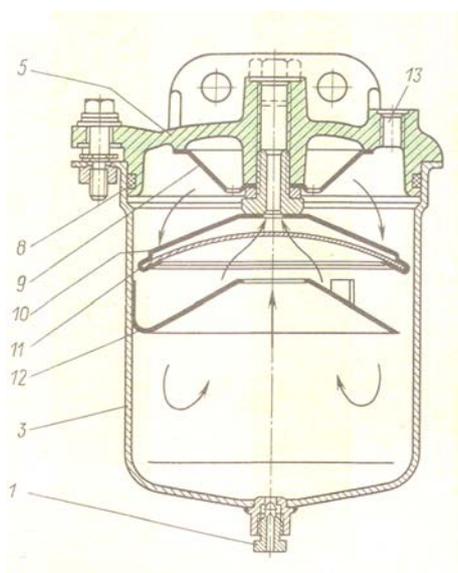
Фильтр тонкой очистки топлива: 1 – сливная пробка; 3 – корпус; 5 – крышка; 8 – прокладка; 9 – распылитель; 10 – отражатель; 11 – фильтрующая сетка; 12 – успокоитель; 13 – отверстие
